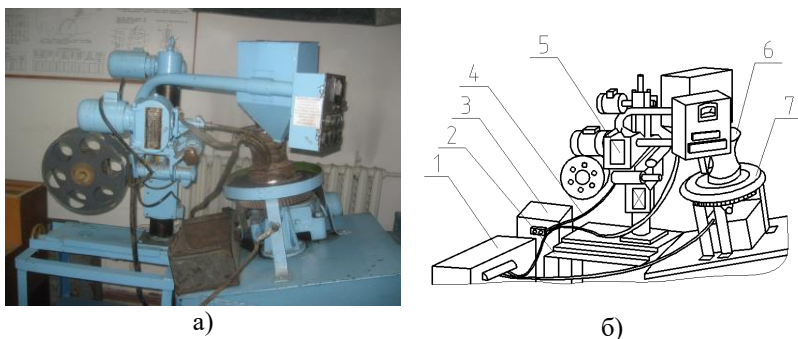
Загальний вигляд лабораторної установки для автоматичного наплавлення під шаром флюсу:
